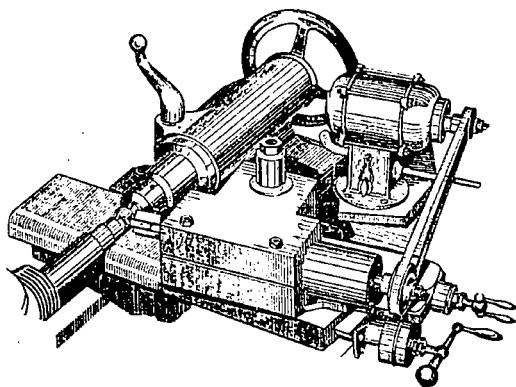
Приспособление для обработки сферических поверхностей вращающимся резцом, установленное на станке.
